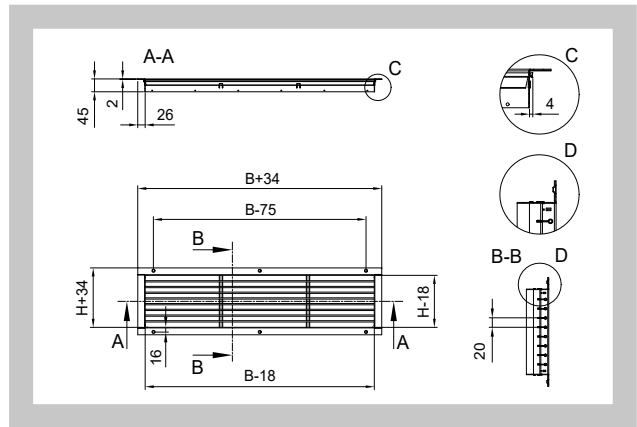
Einstellbare Lamellen horizontal - einreihig
